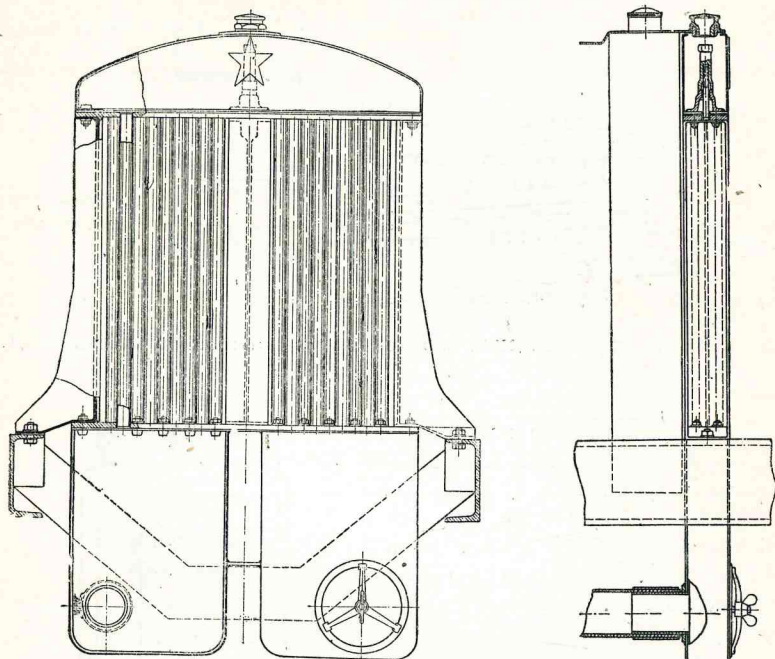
Комбинированный поверхностный очиститель Панар-Левассор:
